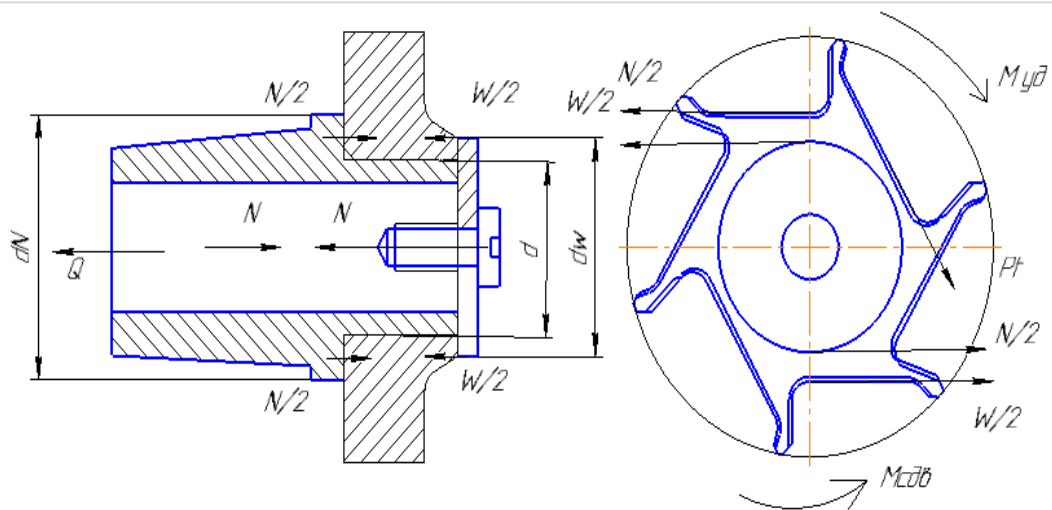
Силы, действующие на заготовку и приспособление
